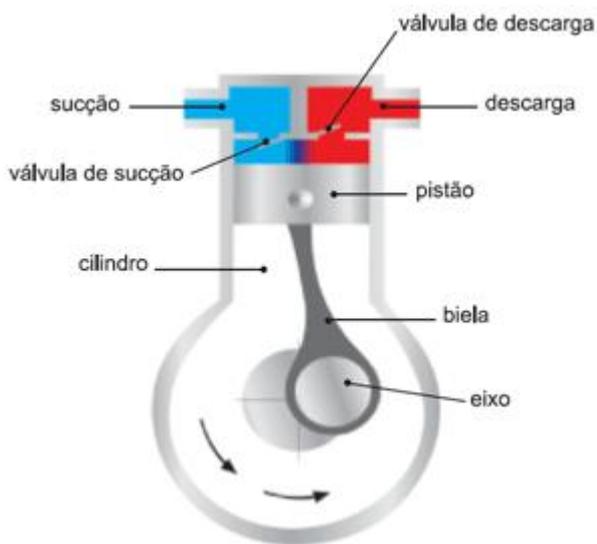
Croqui de um compressor de pistão. Fonte: Máquinas Missão.
